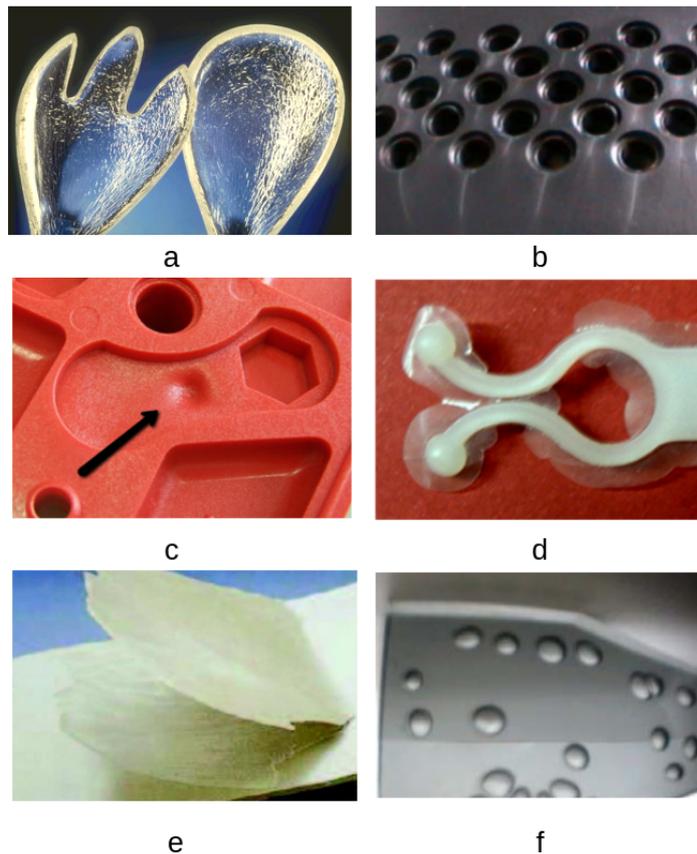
Algunos defectos del moldeo por inyección. a) Fracturas, b) Líneas de soldadura, c) Rechufe, d) Rebabas, e) Delaminación, f) Aire atrapado
